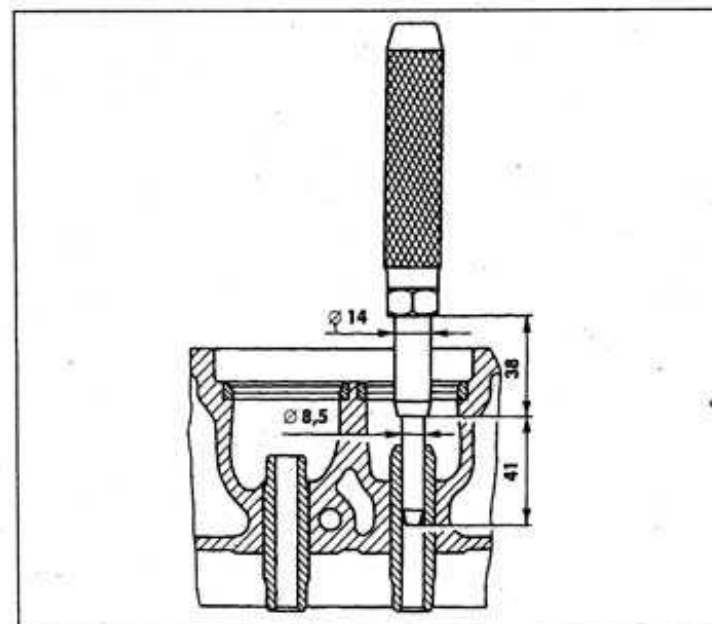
Выпрессовка направляющих втулок клапанов
